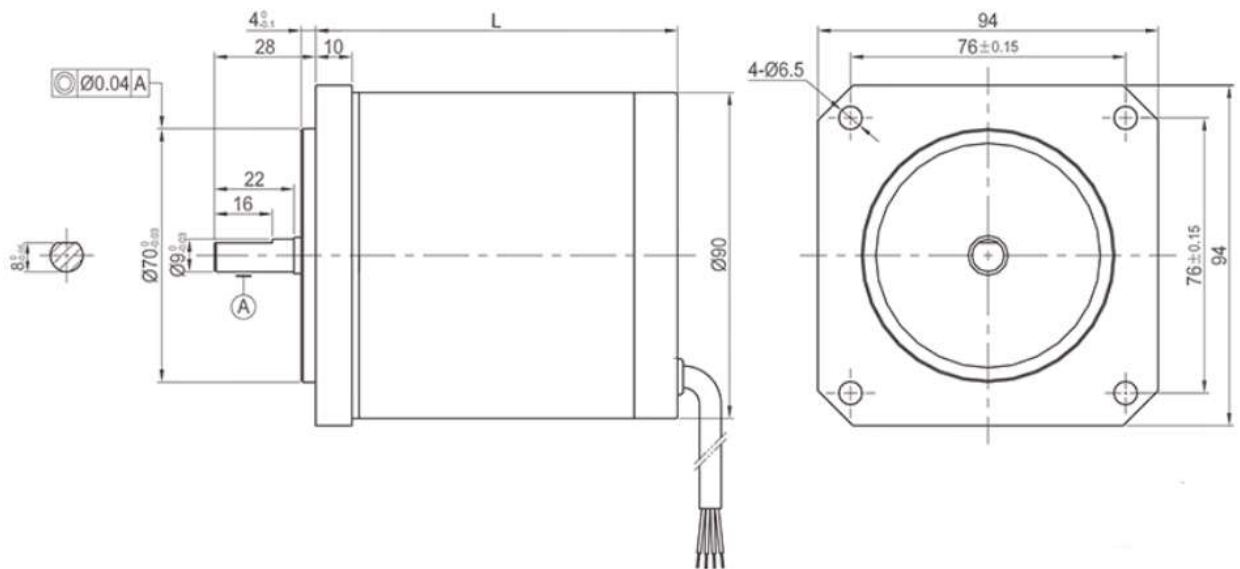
Зовнішній вигляд крокового двигателя двигуна SiaoKe 90TDY060D4-2
